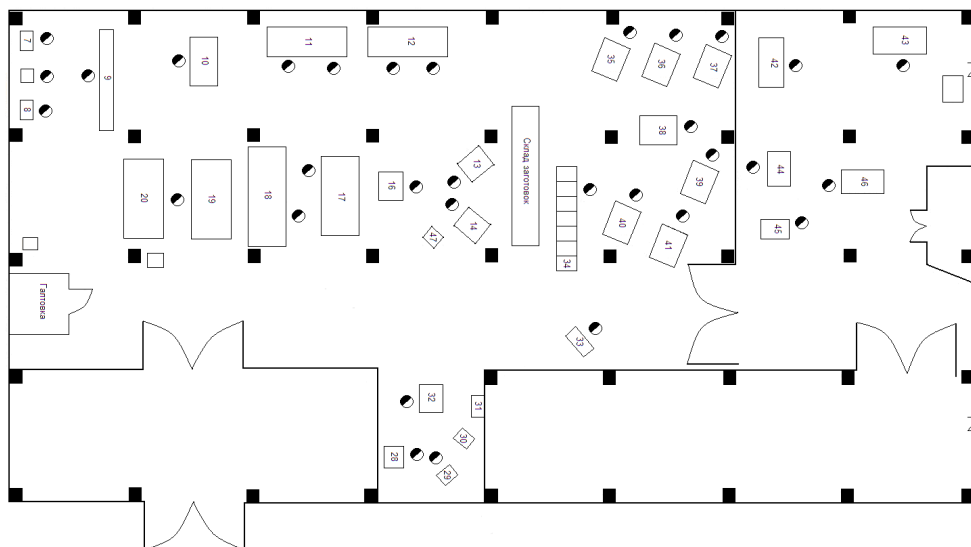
Цех №11 механічної і термічної обробки ріжучого інструменту
